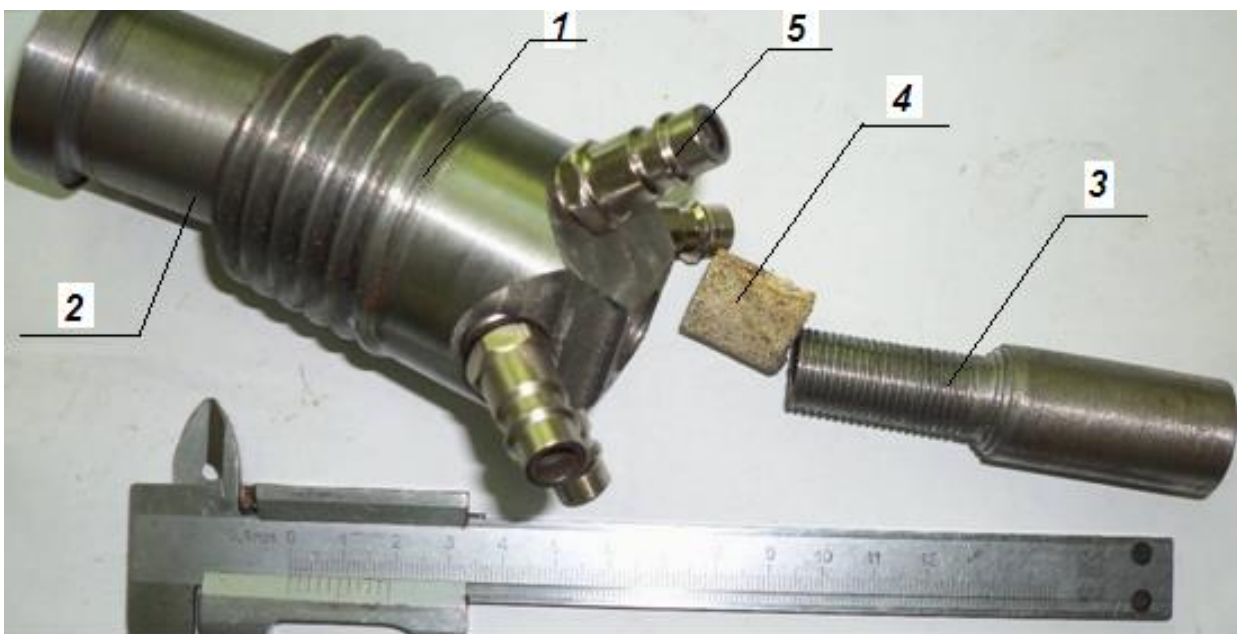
Виготовлені основні частини нової конструкції сопла абразивоструменевої машини
